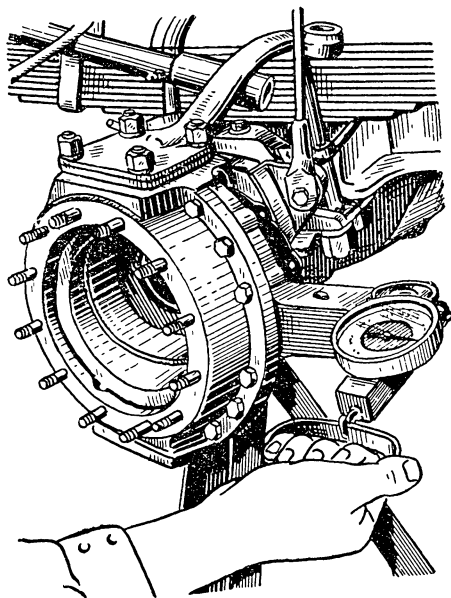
Проверка затяжки подшипников шкворней автомобиля ГАЗ-63 с помощью динамометра
